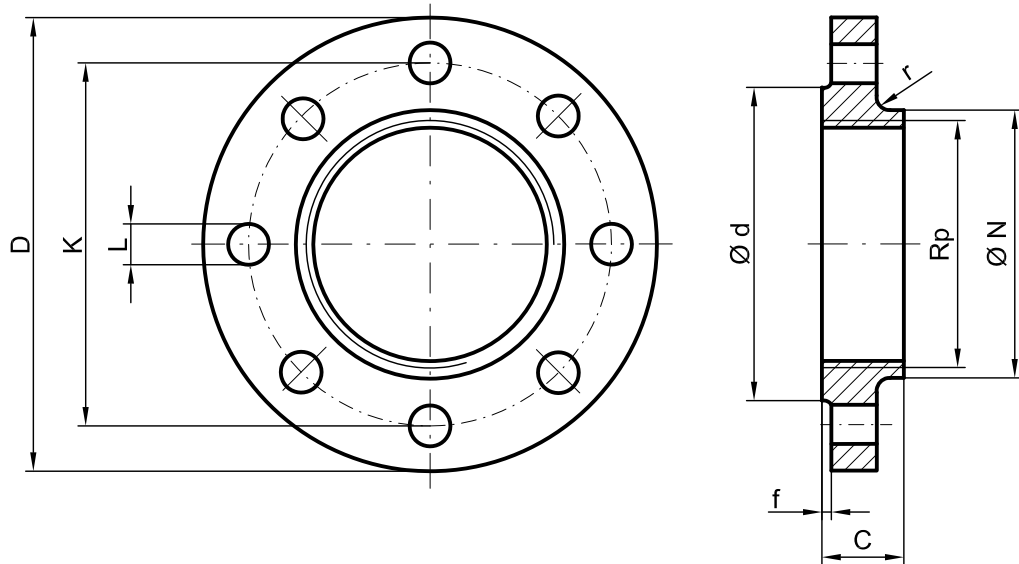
Gewindeflansch mit Ansatz – Typ 13 aus Gusseisen
